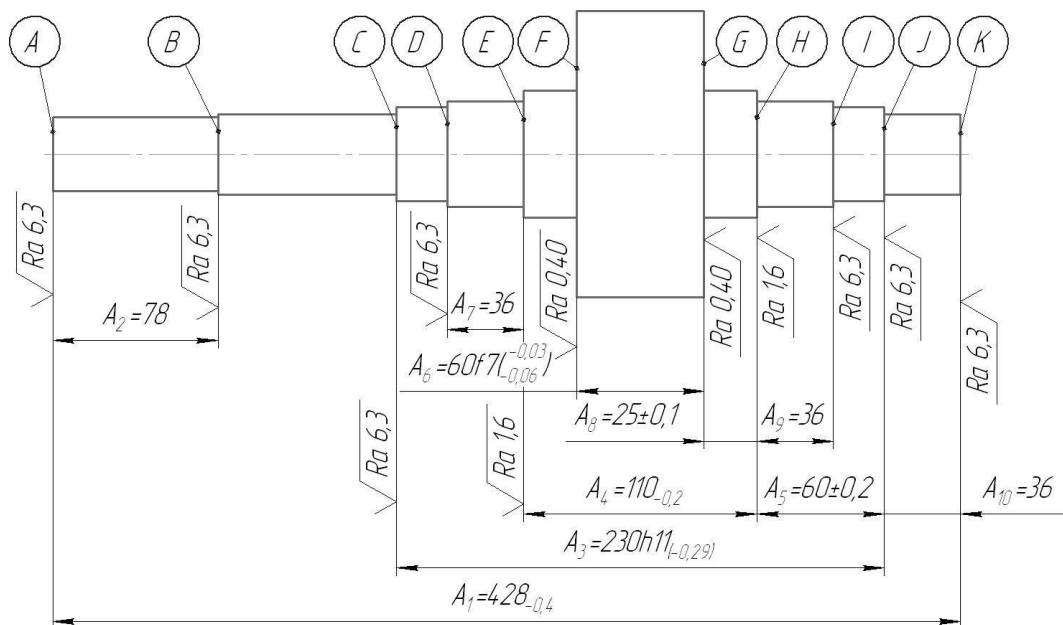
Шестерня з індексацією поверхонь та конструкторських розмірів
